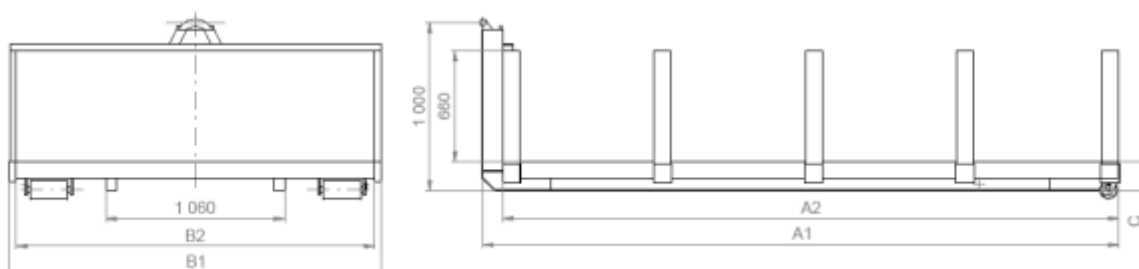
Veľkoobjemový kontajner so sklápnými bočnicami [22]
